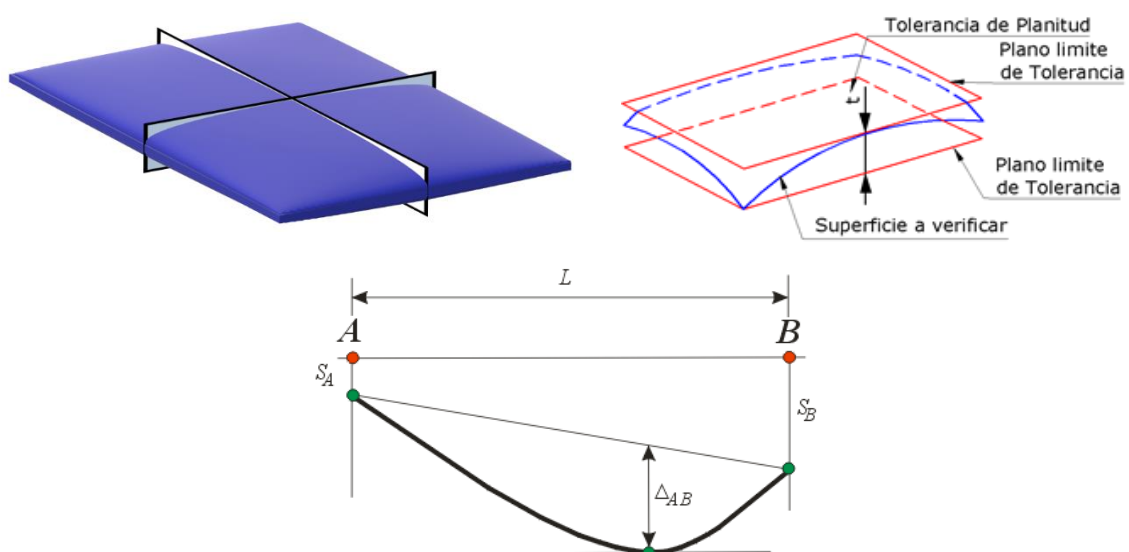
Figura BB: Forma final de la placa de RTM, tolerancia dimensional y deflexión relativa en placa
